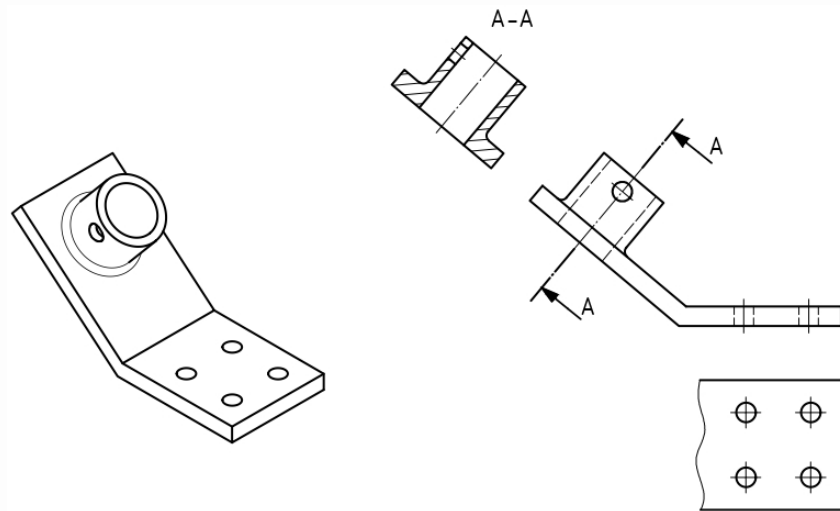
Corte auxiliar com visão posterior ao plano de corte
